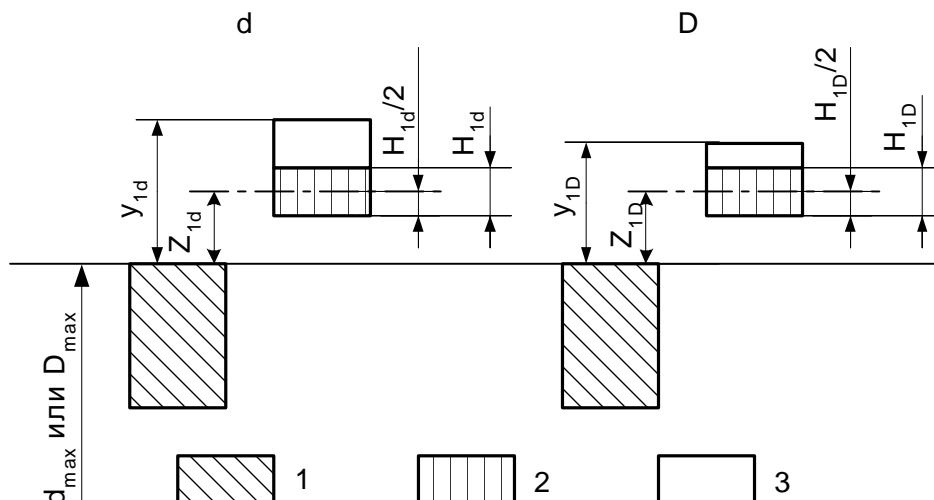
Схема расположения поля допуска размера  $b_k$  калибра-пробки
